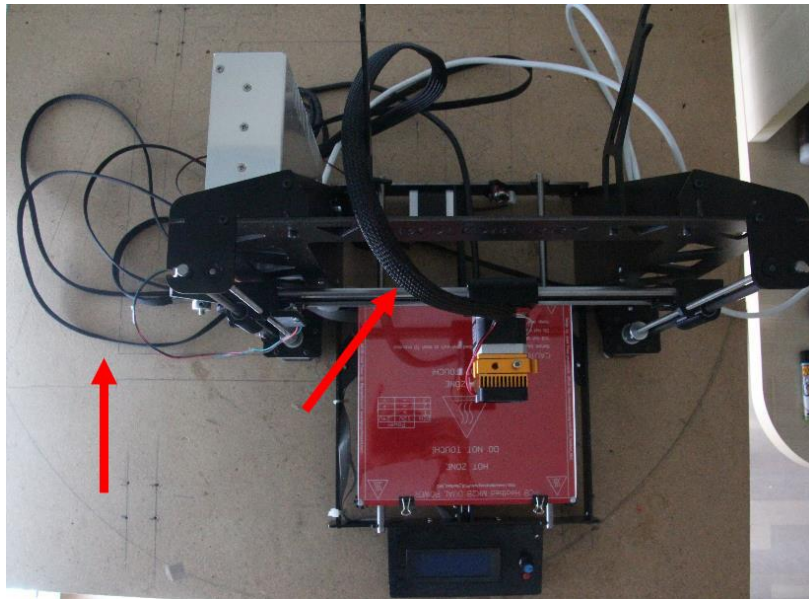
Portacables flexible para cableado del extrusor y de los motores.
